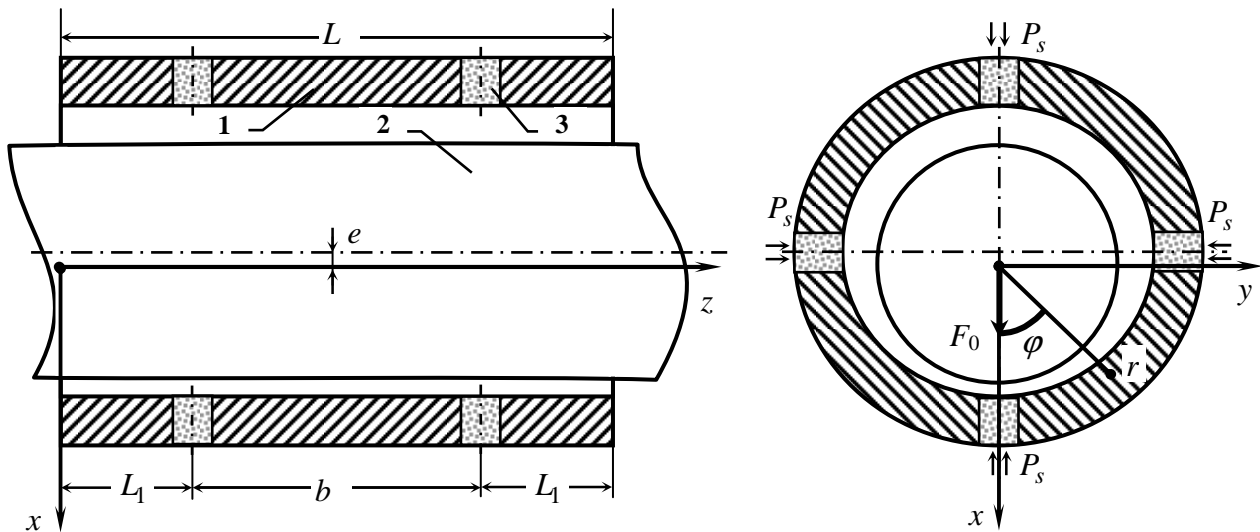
Газовый статический подшипник с двумя рядами пористых вставок:
